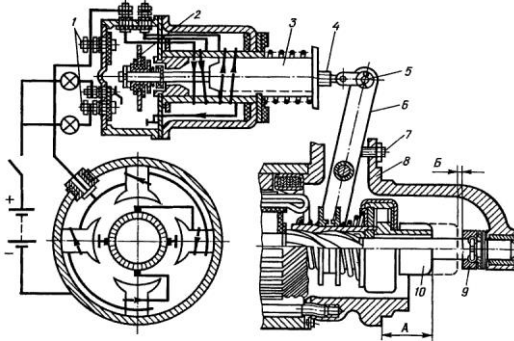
Схема регулювання приводу стартерів 1 – нерухомий контакт стартера; 2 – рухомий контакт тягового реле; 3 – якірець тягового реле; 4 – гвинт; 5 – палець; 6 – важіль приводу; 7 – регульовальний гвинт; 8 – кришка стартера; 9 – упорне кільце; 10 – шестирня приводу
